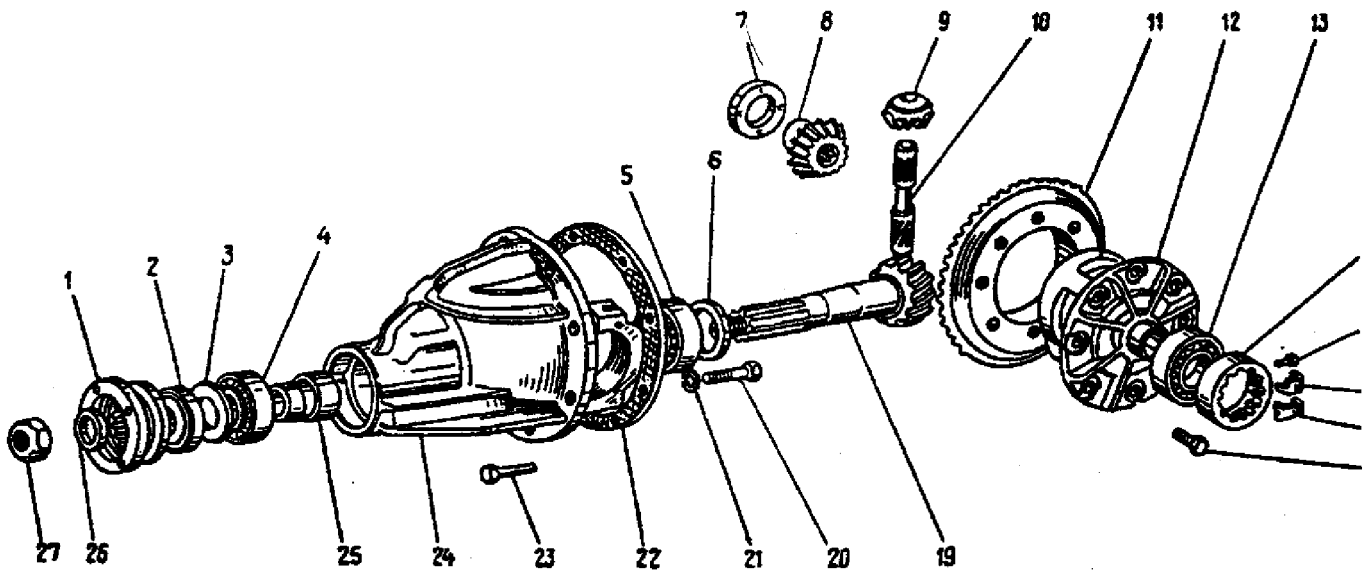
Conjunto porta-diferencial: 1 - flange do pinhão; 2 - vedador; 3 - defletor de óleo; 4 - rolamento dianteiro; 5 - rolamento traseiro; 6 - anel de ajuste do pinhão; 7 - arruela de encosto da planetária; 8 - planetária; 9 - satélite; 10 - eixo das satélites; 11 - coroa; 12 - caixa do diferencial; 13 - rolamento lateral da coroa; 14 - porca de ajuste; 15 - parafuso de fixação da placa de retenção; 16 - placa de retenção; 17 - placa de retenção; 18 - parafuso de fixação da coroa; 19 - pinhão; 20 - parafuso de fixação da capa; 21 - arruela elástica; 22 - junta; 23 - parafuso de fixação do porta-diferencial; 24 - porta-diferencial; 25 - bucha espaçadora; 26 - arruela plana; 27 - porca do flange do pinhão
